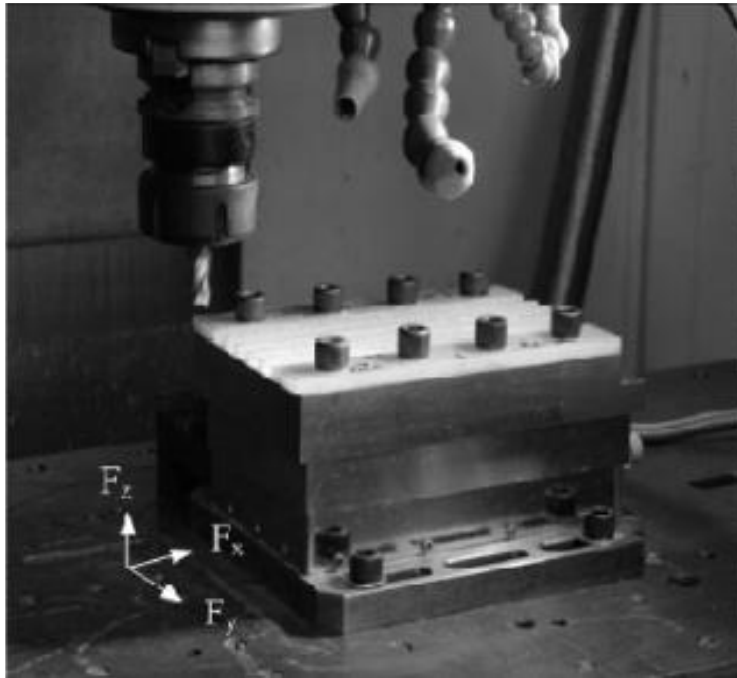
Кінцеве фрезерування скловолоконних композитів
